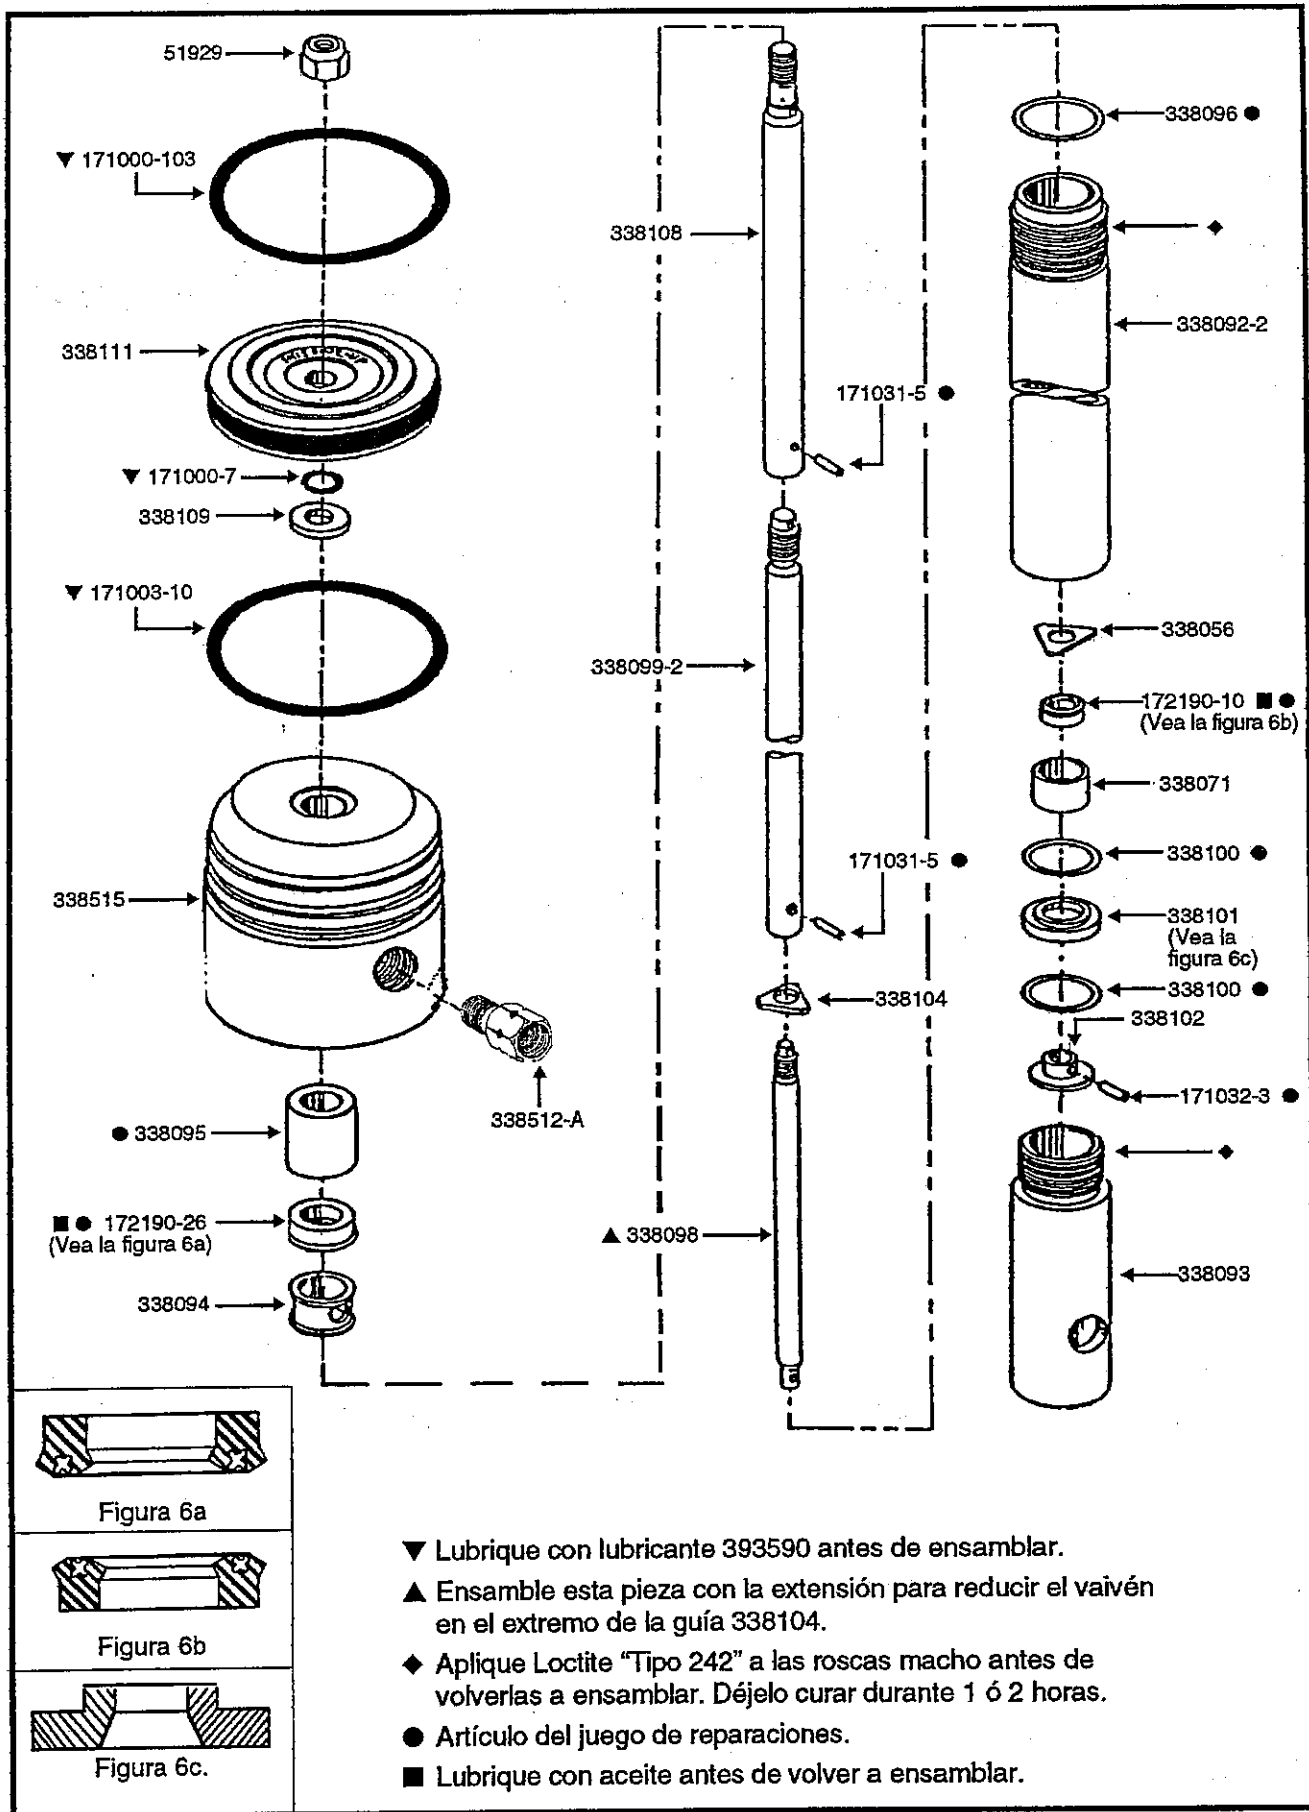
Ensamblaje del tubo de bombeo 338087-B11
